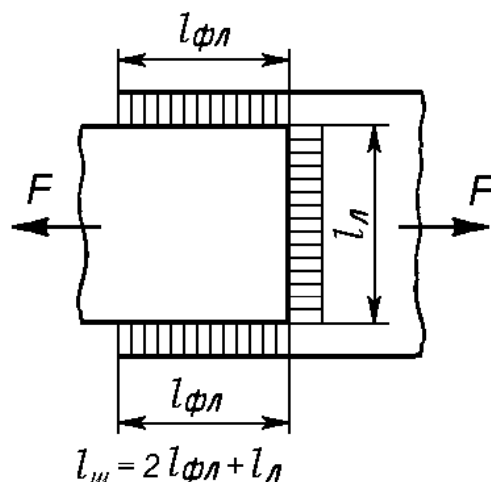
Комбинированный сварной шов нахлесточного соединения
